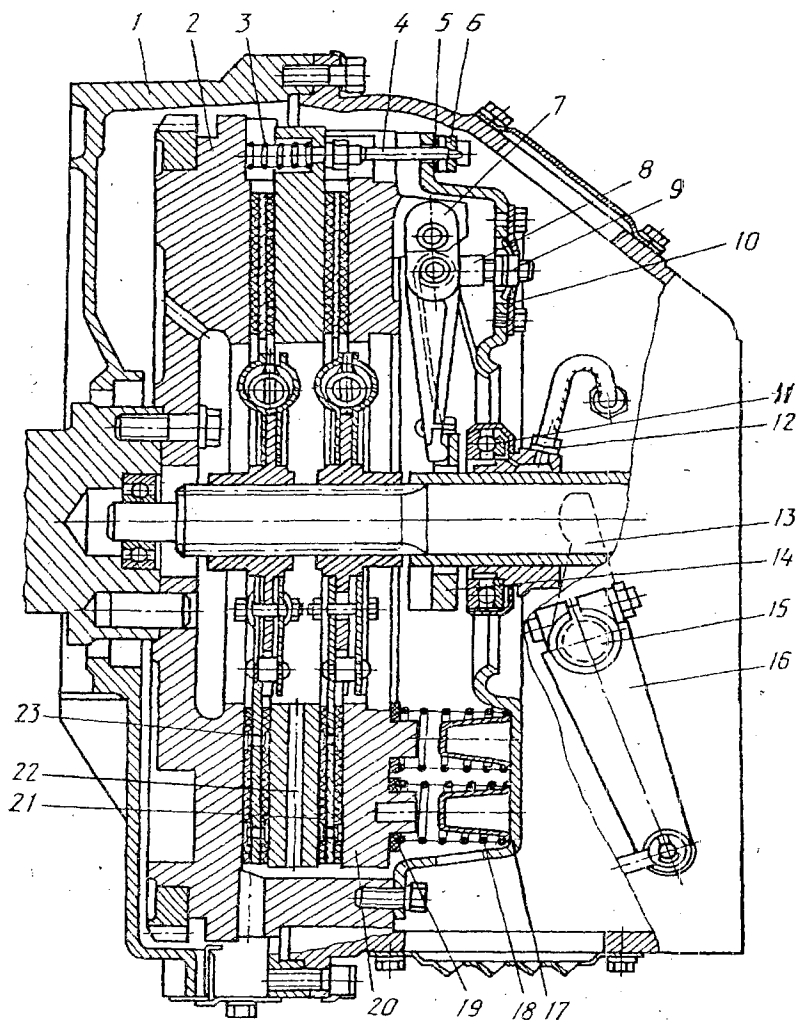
Сцепление двухдисковое с периферийными пружинами:
